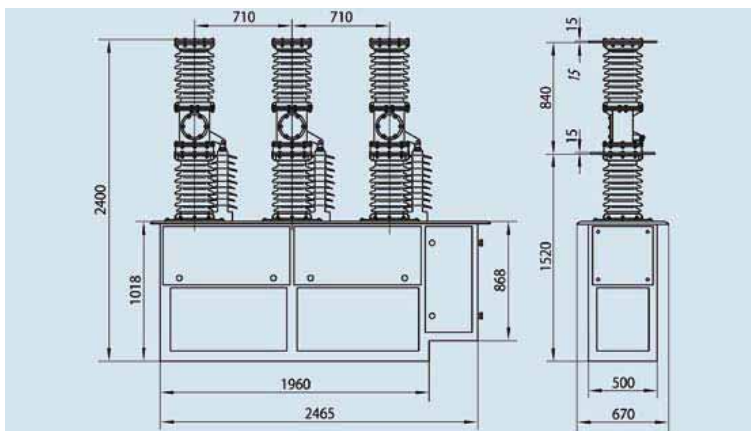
Внешний вид и размеры выключателя ZW7-40.5
